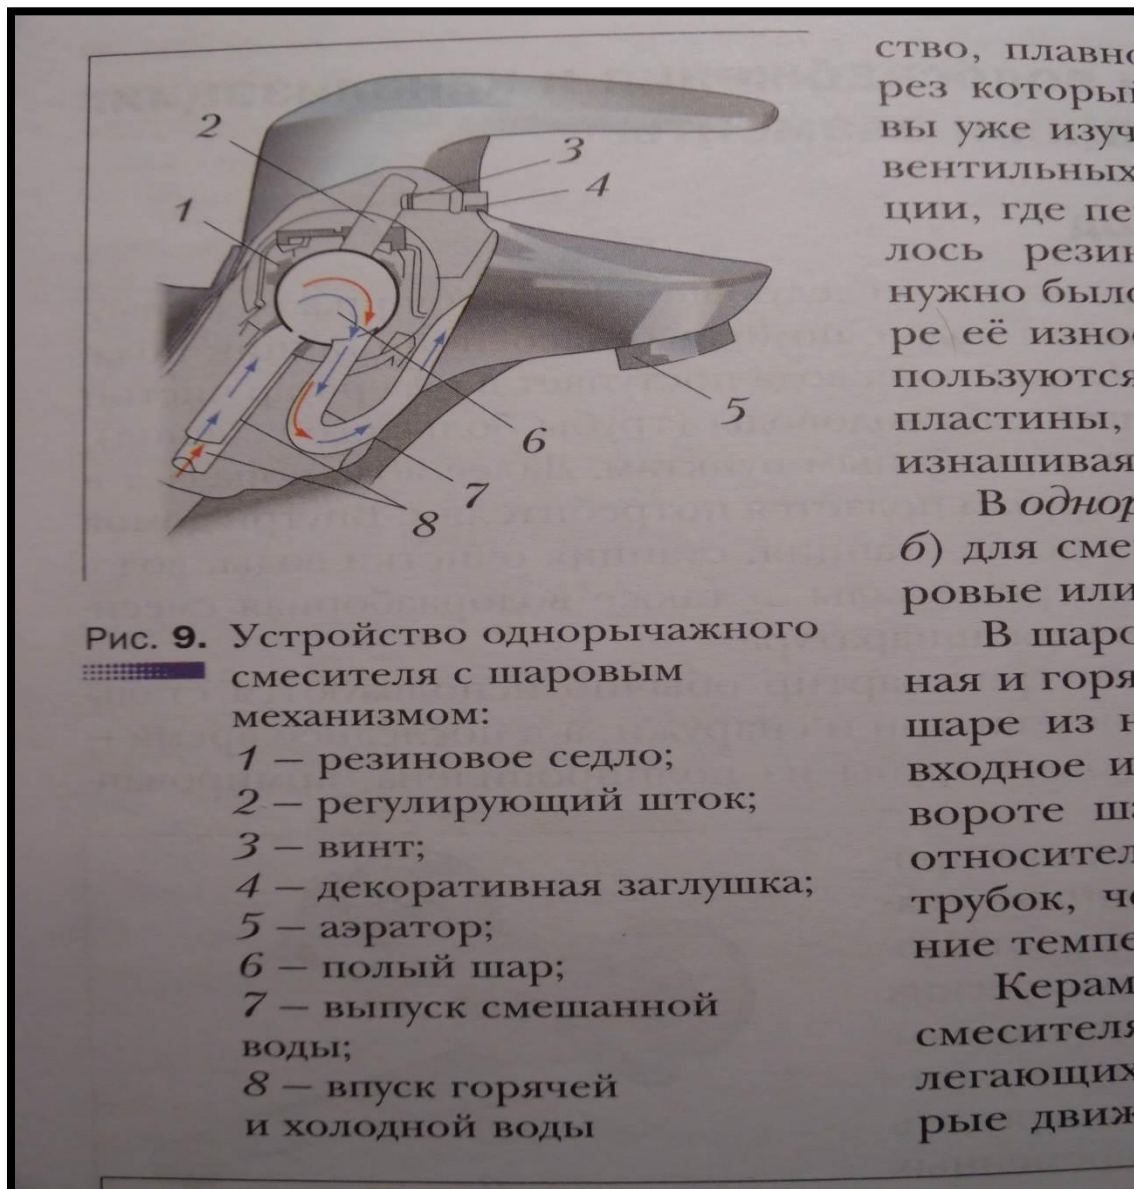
Устройство однорычажного смесителя с шаровым механизмом:
